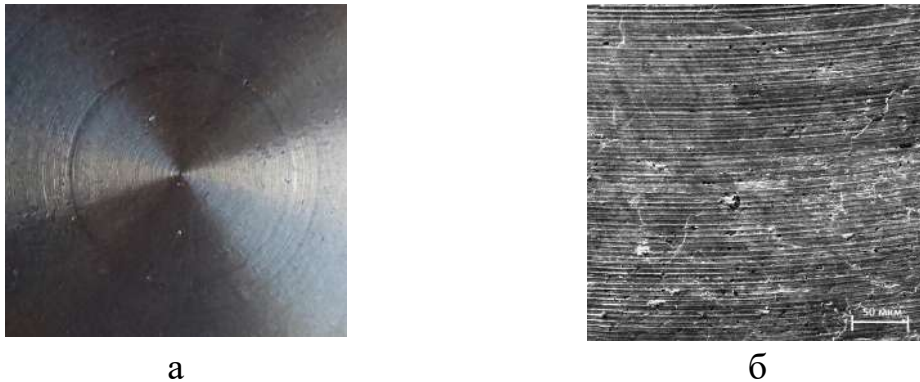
Поверхность образца пористого титана с размером фракций порошка 0,4–0,63 мм, подвергнутая механической обработке: а – общий вид поверхности образца; б – образец при увеличении $\times 65$
